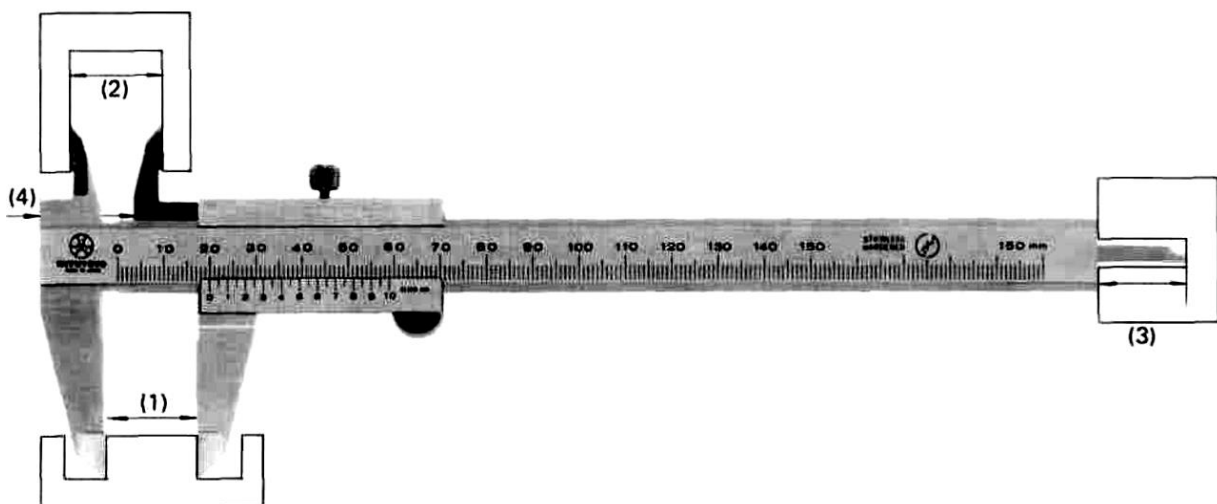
Вимірювання штангенциркулем з ноніусом
